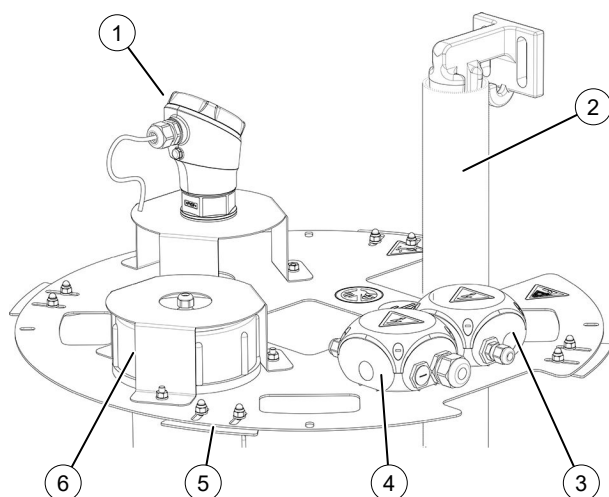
Plaque de fixation de capteurs cuve enterrée en PE
